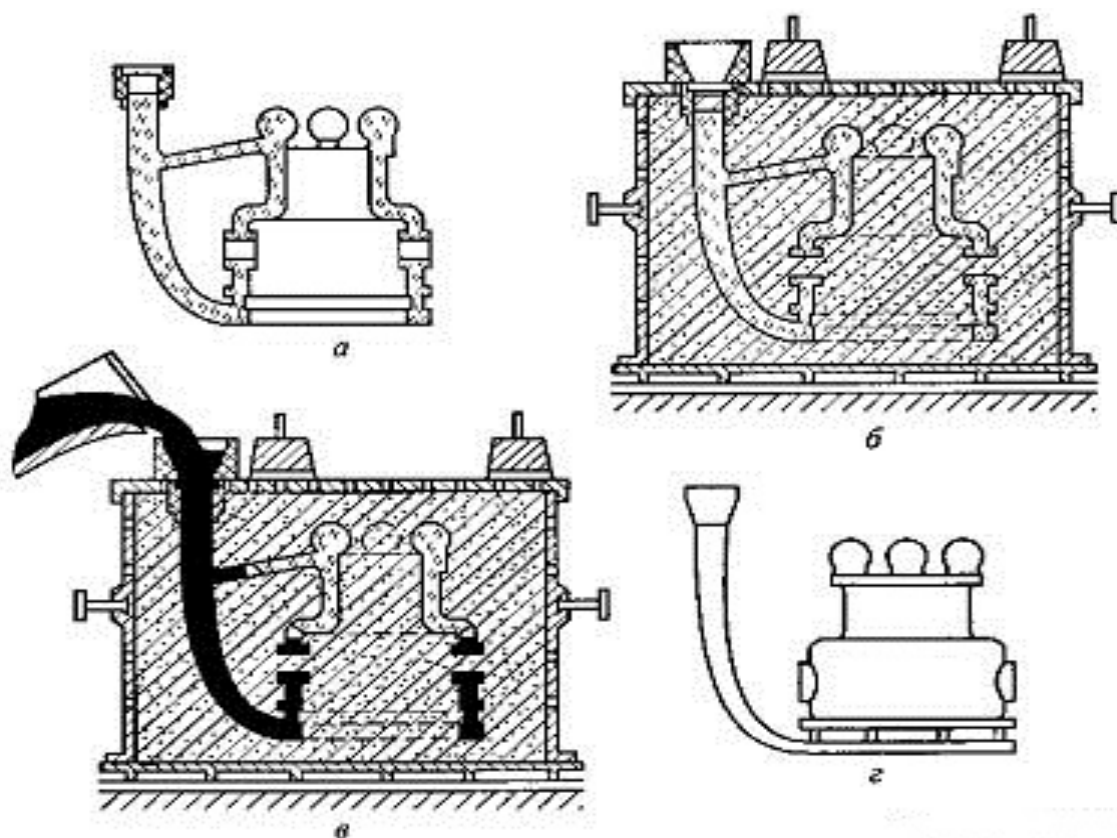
Схема изготовления отливки по газифицируемой модели:
